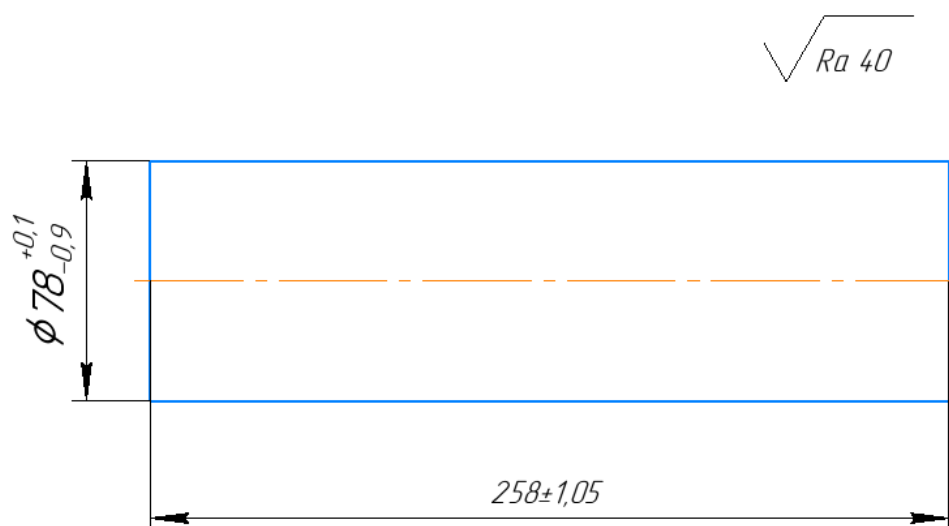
Эскиз заготовки детали «Вал механизма поворота»
